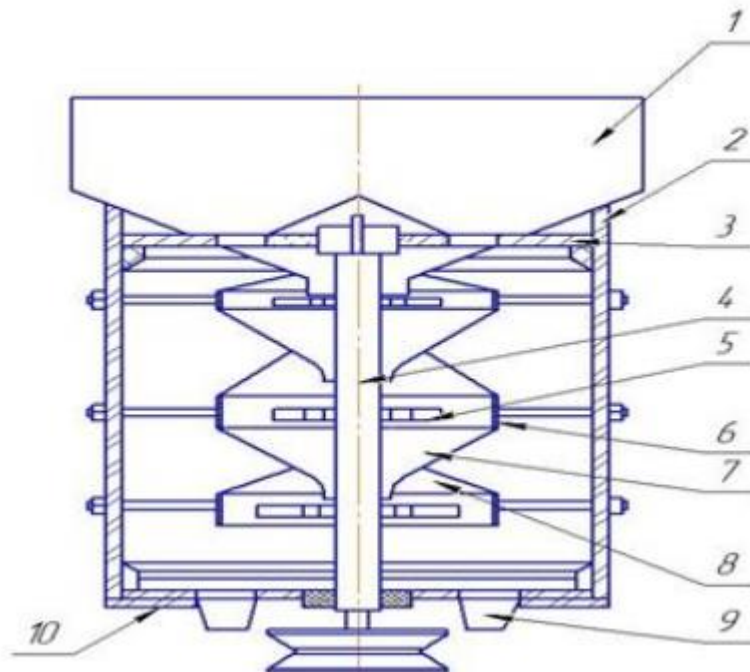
Схема відцентрової багатостадійної дробарки зерна: 1-завантажувальний бункер; 2 – циліндричний корпус; 3 – верхні плити; 4 – вертикальний вал; 5 – розгонні диски; 6 – відбійні плити; 7 – корпусні воронки 8 – скатні дошки; 9 – відвідні патрубки; 10 – нижні опорні плити
